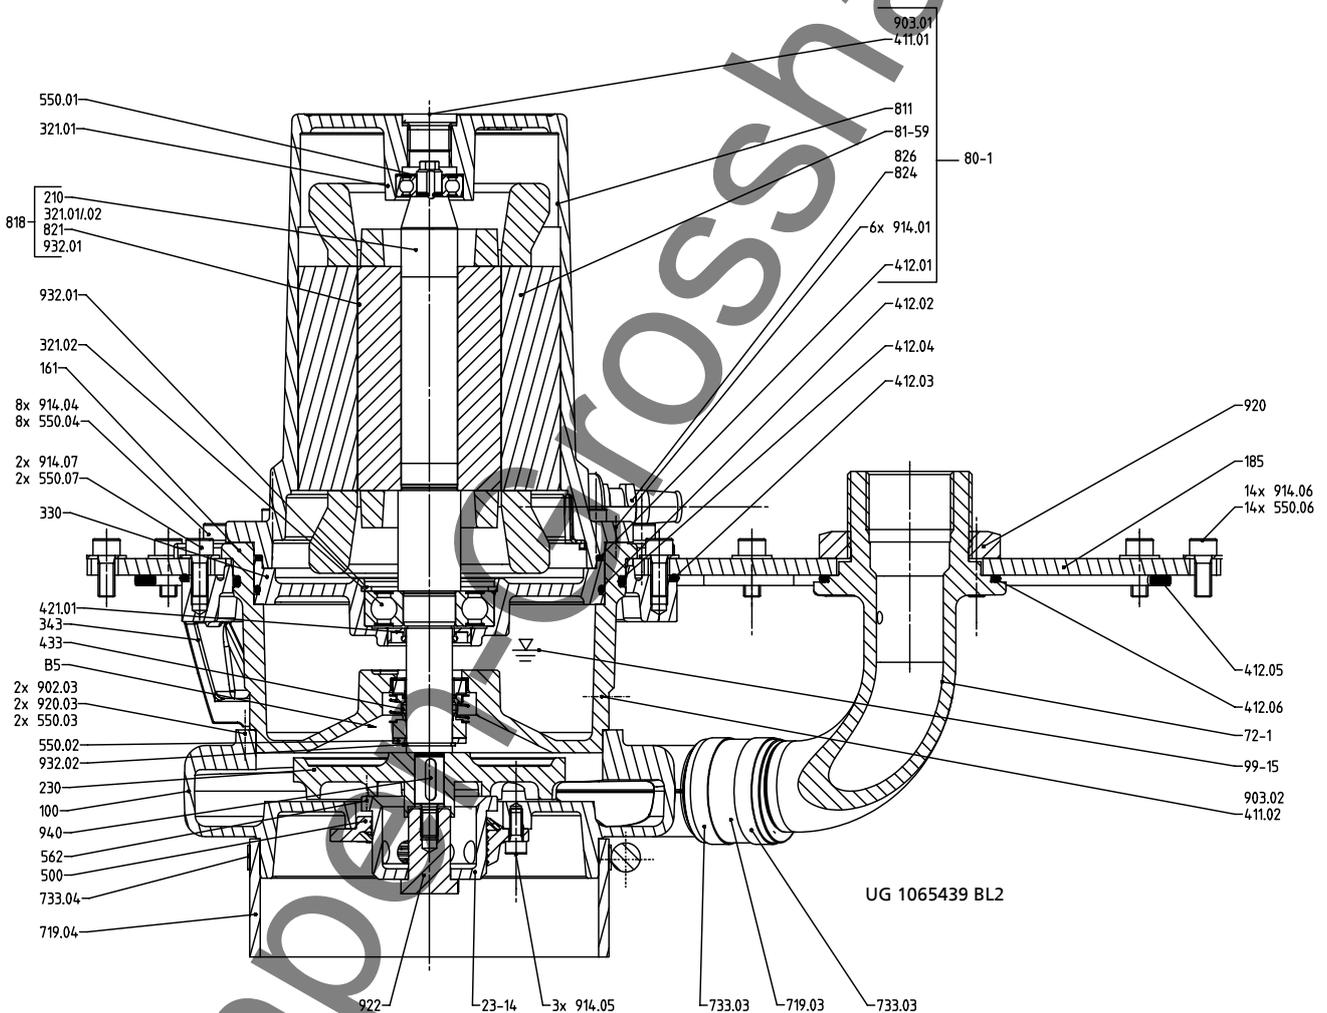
Gesamtzeichnung US100, UZS150 - Laufteil
